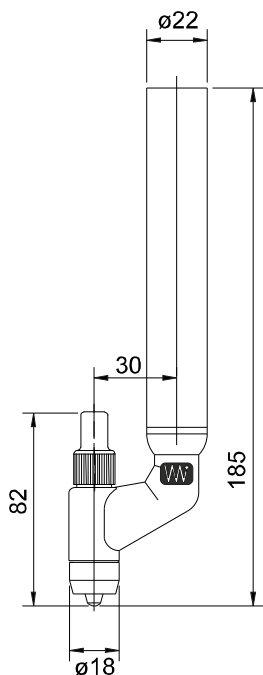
PWM 150 горелка для машинной сварки
